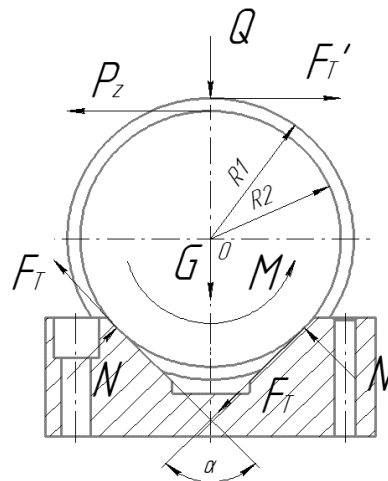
Схема закріплення деталі в пристрої.
